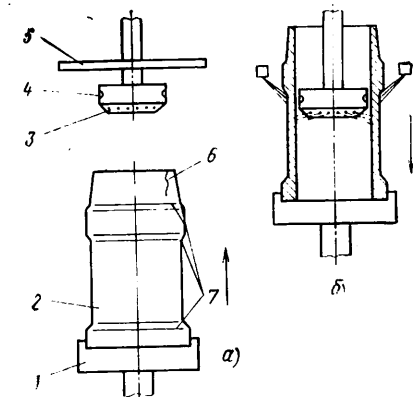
Схема процесса закалки: а — положение заготовки перед закалкой; б — положение заготовки в момент закалки
